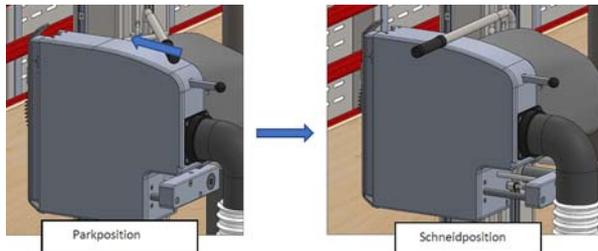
Positionieren des Werkstücks auf der Plattensäge
